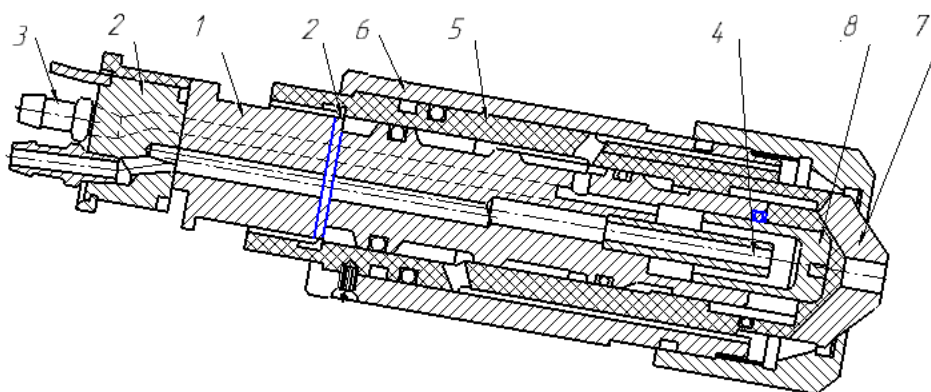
Чертеж режущей головки, где 1-электродержатель, 2- переходник, 3- штуцер, 4- трубка, 5- изолятор, 6-корпус, 7- сопло, 8- электрод.
